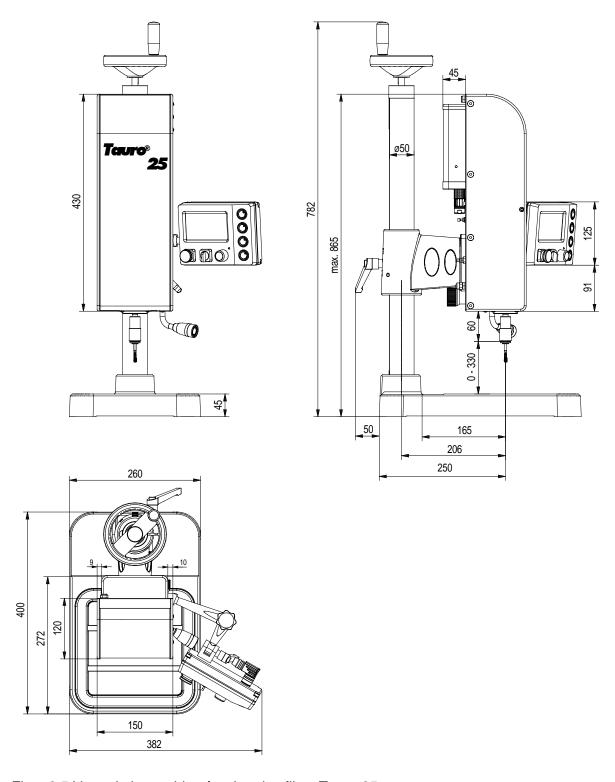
Vues de la machine à usiner les filets Tauro 25
